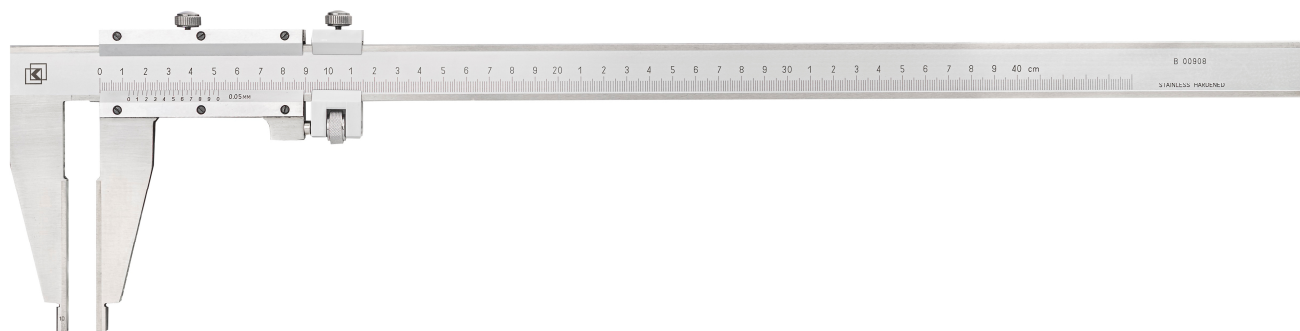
Общий вид штангенциркулей ШЦ-III
